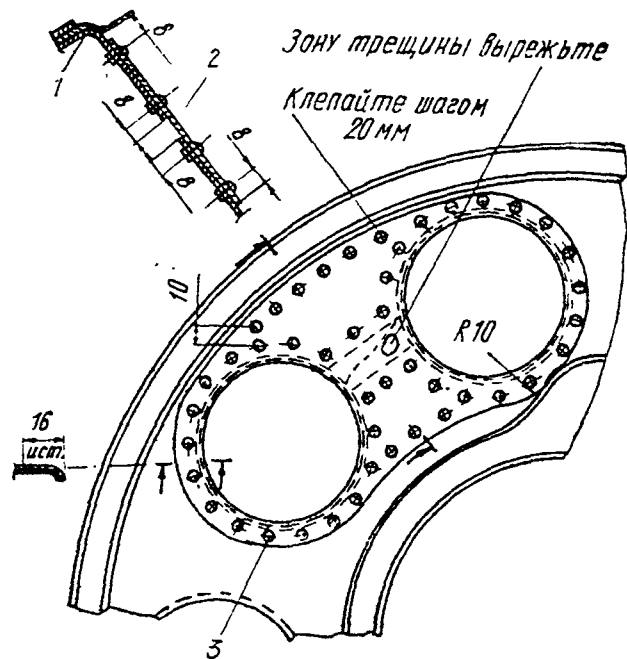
Ремонт диафрагмы обтекателя редуктора при
